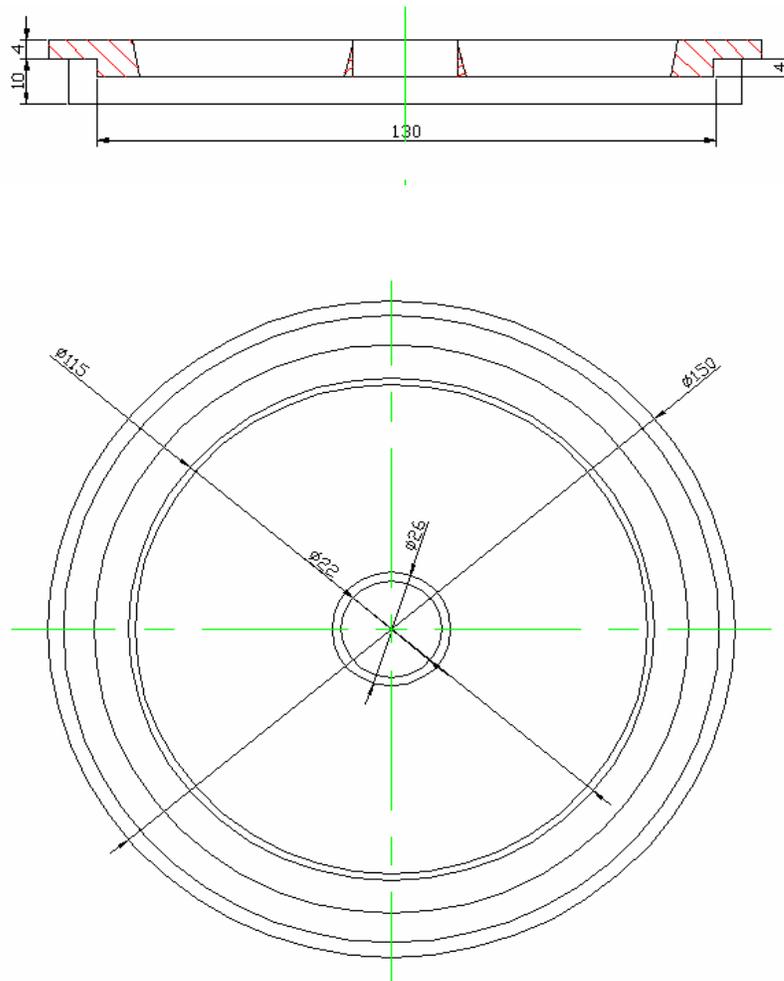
Molde ensamblado. Vistas principales en 2D
